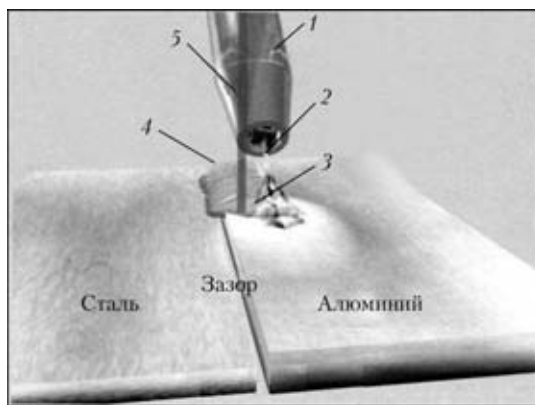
Схема гибридной лазерно-дуговой сварки [17]: 1 — сварочная горелка; 2 — присадочная проволока; 3 — сварочная ванна; 4 — сварной шов; 5 — луч лазера
